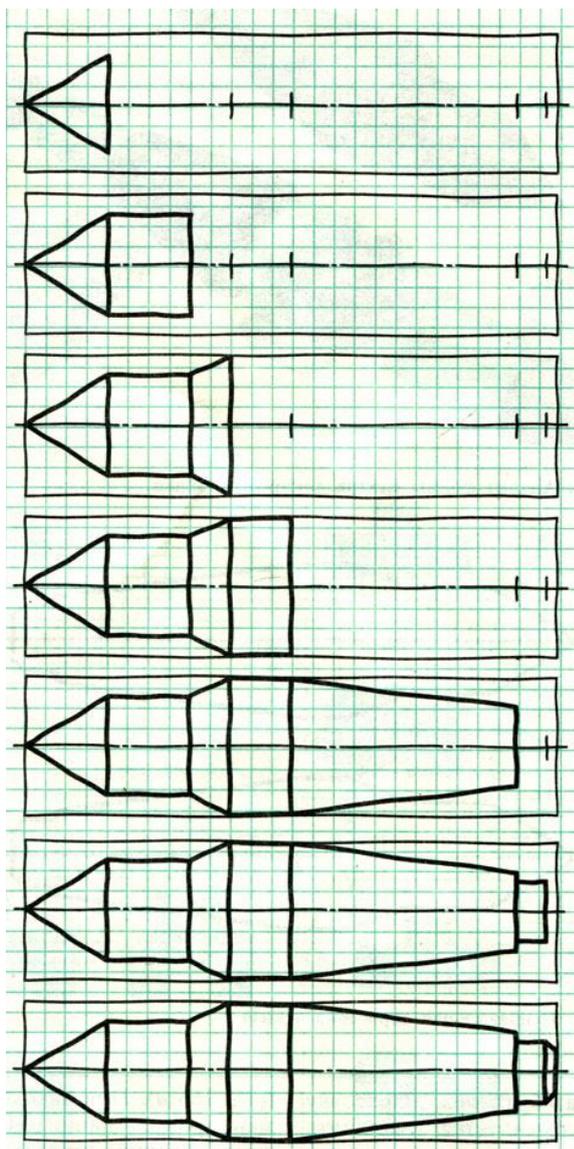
Последовательность зарисовки эскиза центра токарного станка
